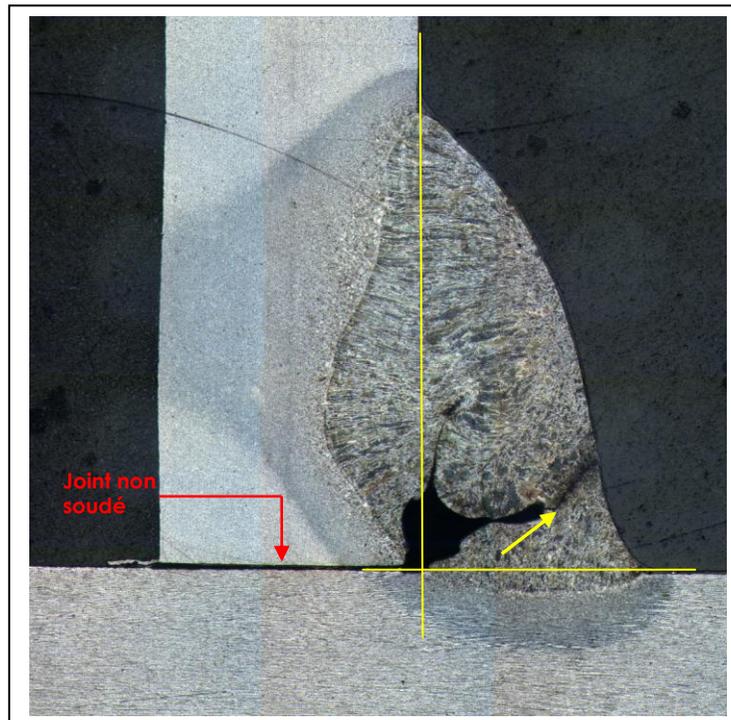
Fissure à la racine du cordon de soudure 1DI - surface ext.
